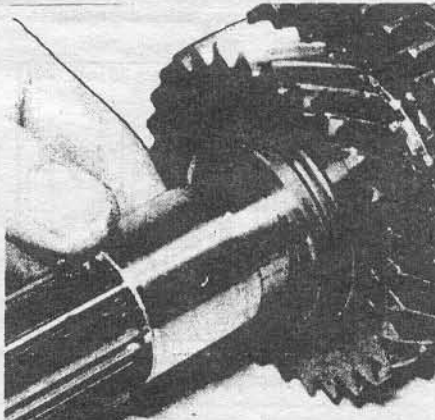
а Установка проставки шестерни 3-й передачи.
